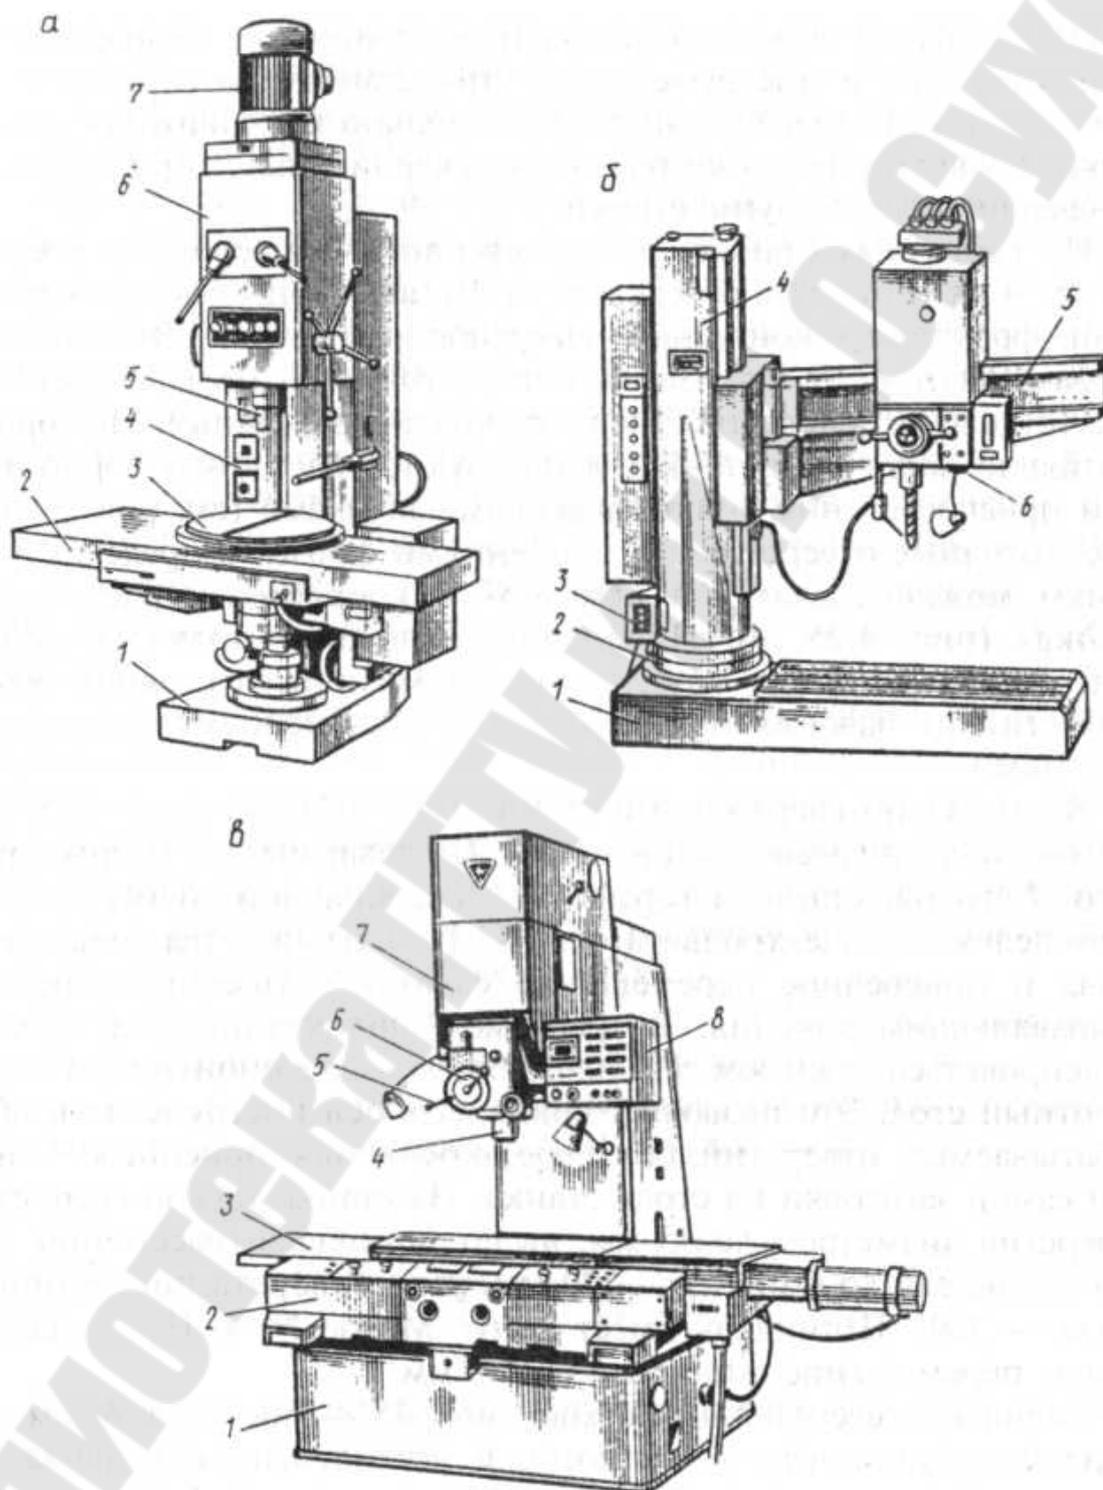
Общий вид станков сверлильно-расточной группы: а – вертикально-сверлильный мод. 2Н135-1; б – радиально-сверлильный мод. 2554; в – координатно-расточной мод. 2А450Ф30
